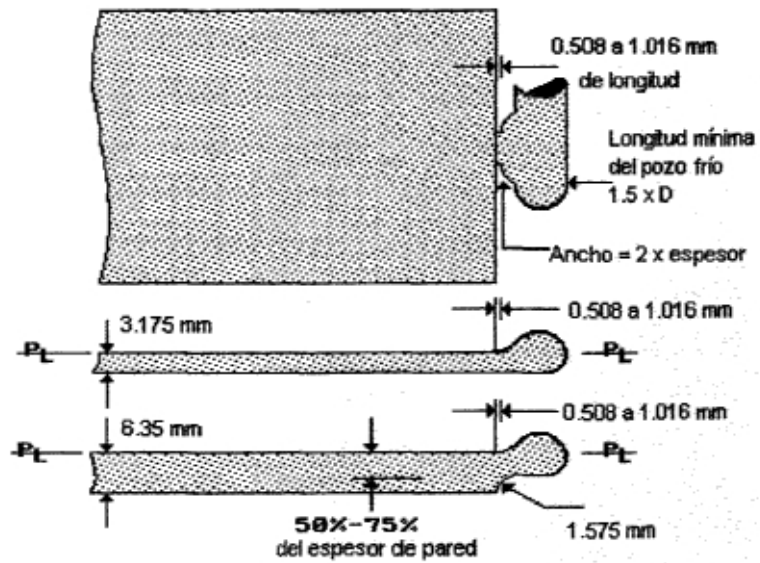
Entrada intermedia entre tipo abanico y laminar.<sup>6</sup>
